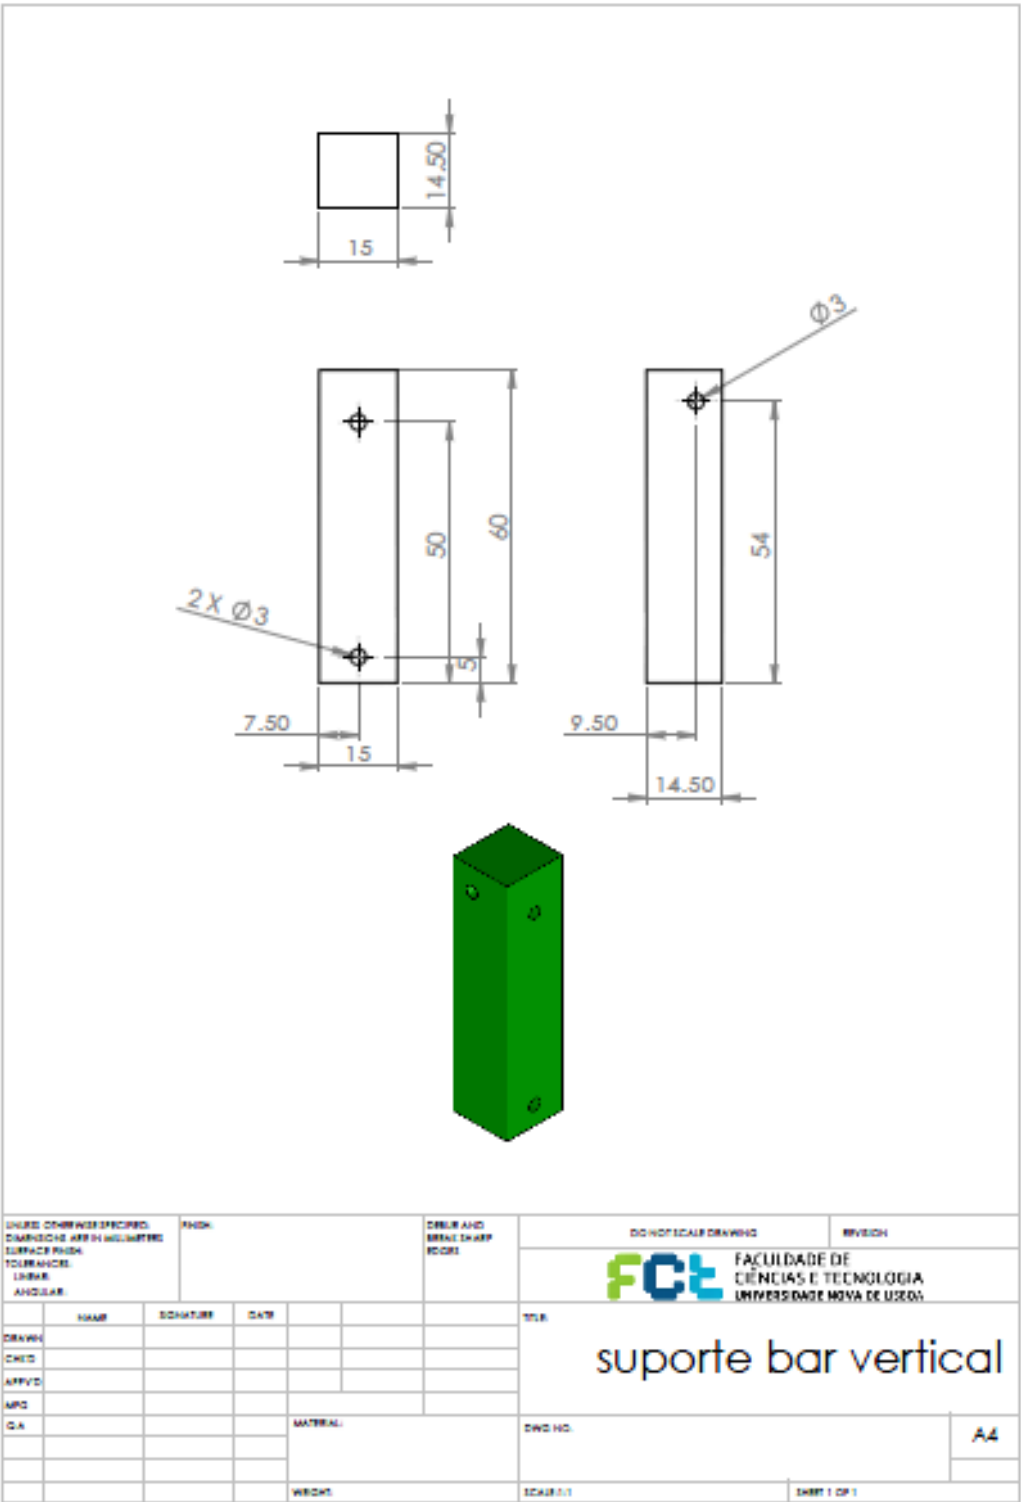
Desenho técnico do suporte do barramento vertical.
